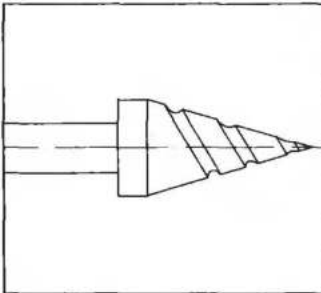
Центр со спиральной канавкой для установки в патрон токарного станка
